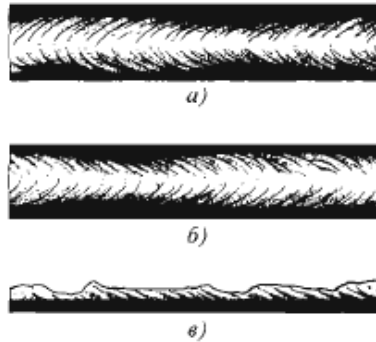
Дефекты формы швов: а - неравномерная ширина шва при ручной сварке; б - то же, при автоматической сварке; в - неравномерная выпуклость - бугры и седловины.
